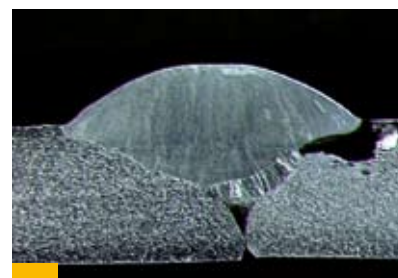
Ungenügende Durchschweißung einer Schweißnaht bietet dem Korrosionsmedium optimale Angriffsfläche
